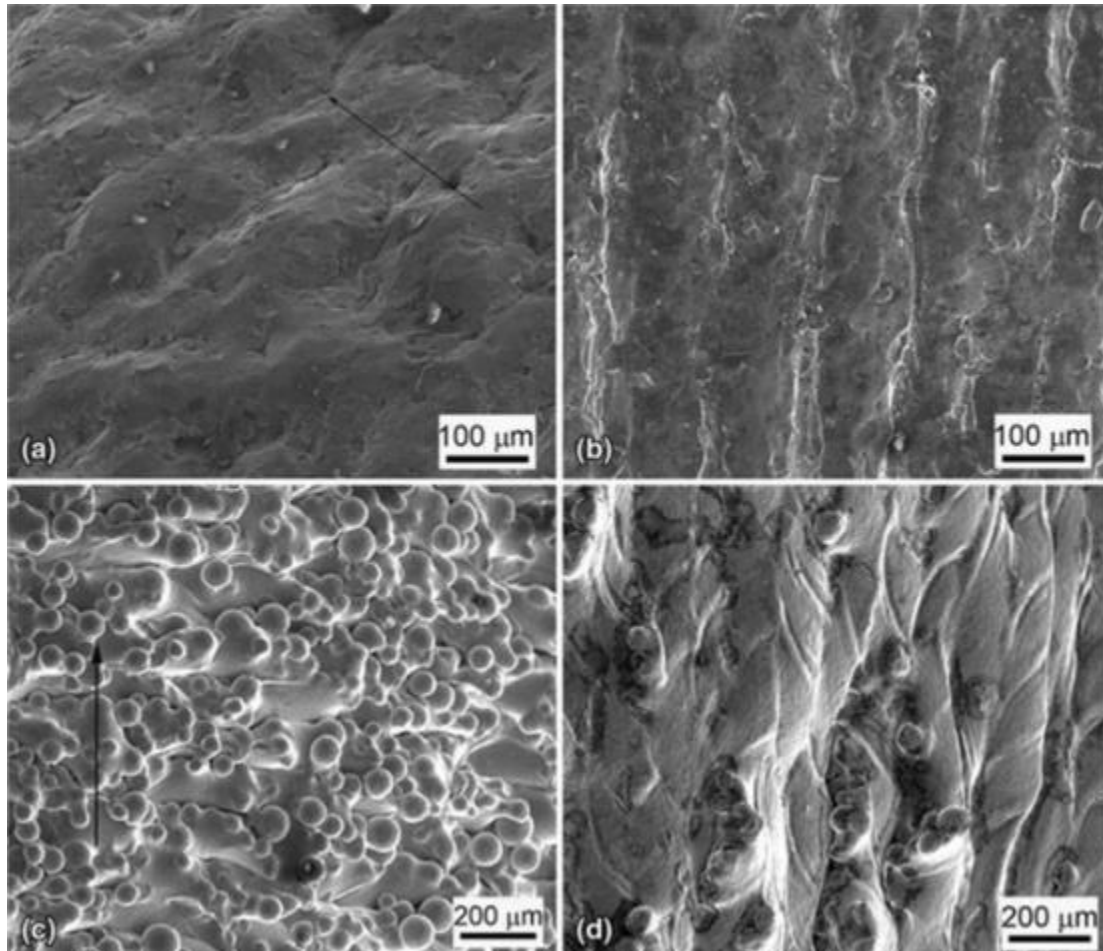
Morfología de la superficie externa de (a) un espécimen SLM construido longitudinalmente, (b) un espécimen SLM construido horizontalmente, (c) un espécimen EBM construido longitudinalmente, (d) un espécimen EBM construido horizontalmente. Para muestras longitudinales, la flecha muestra la dirección de la construcción mientras que, para las muestras horizontales, la dirección de la construcción es perpendicular al plano de la imagen [19].
